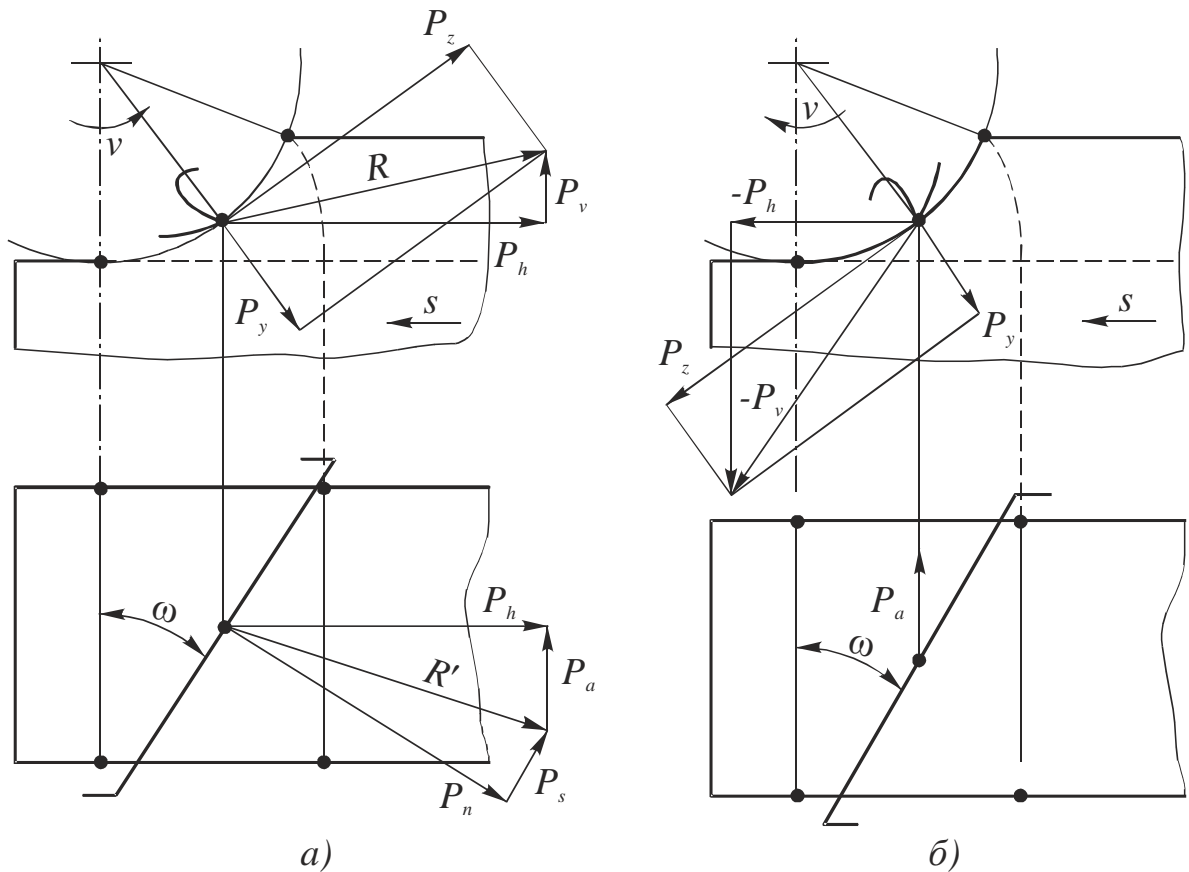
Составляющие силы резания R на винтовом зубе цилиндрической фрезы: a – встречное фрезерование; b – попутное фрезерование
